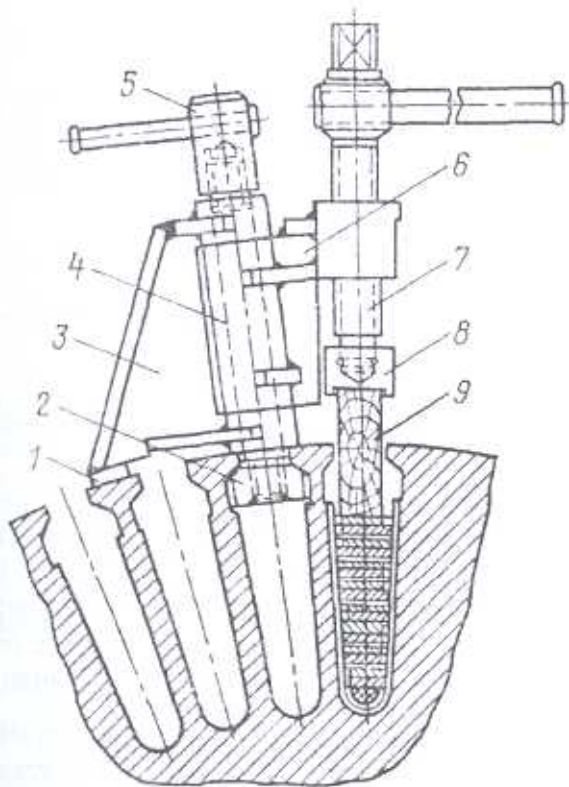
Прессовка пазовой части обмотки ротора домкратом:
